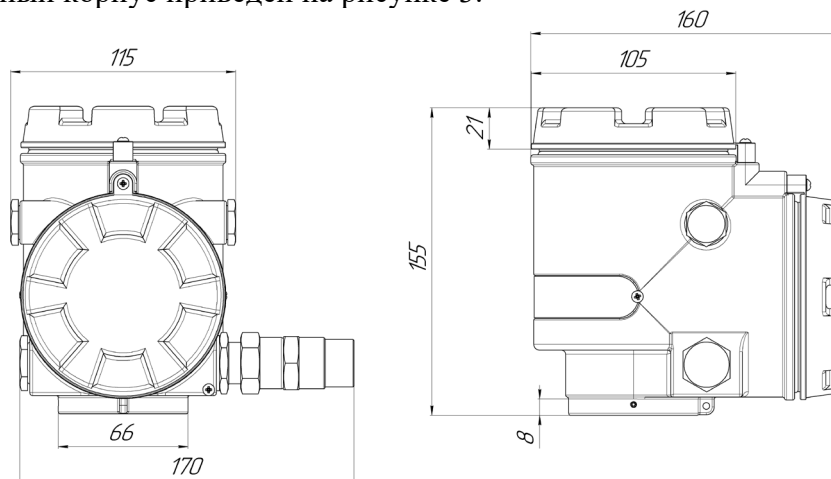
Габаритные размеры двухкамерного корпуса
